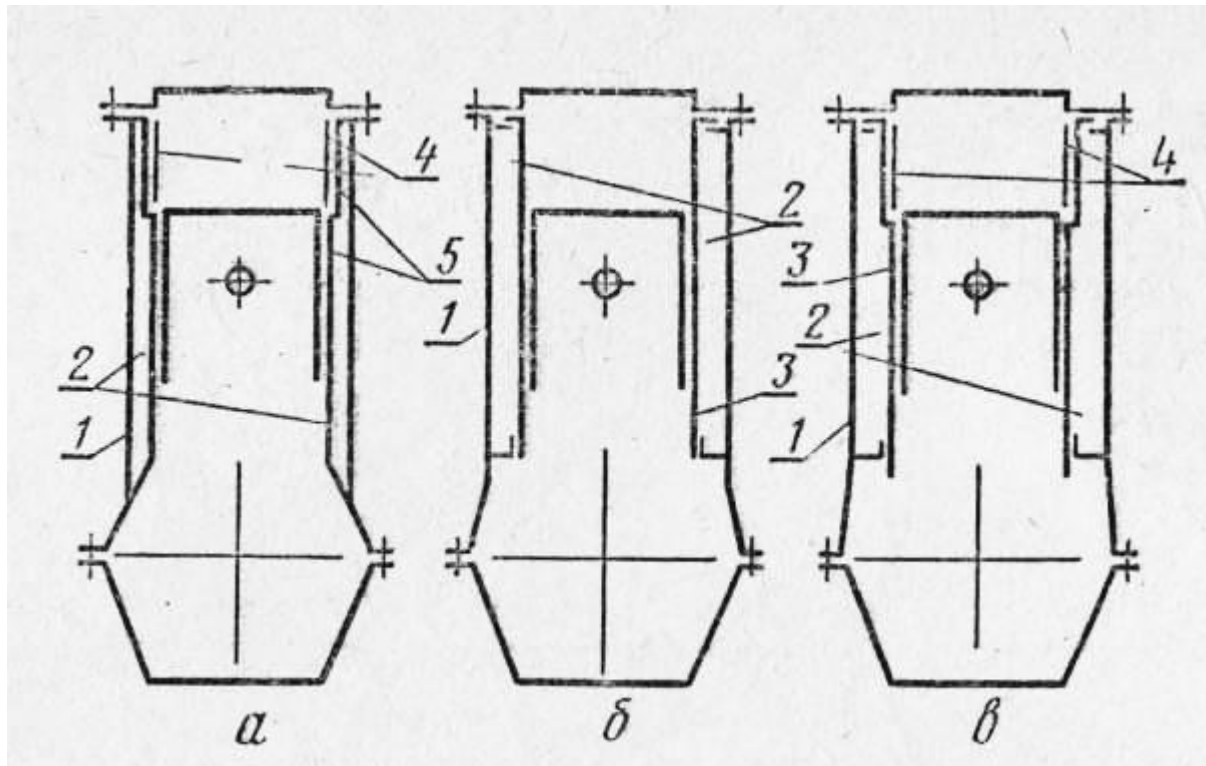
Конструктивные схемы гильз цилиндров: а — цилиндр с короткой сухой гильзой; б — цилиндр с вставной гильзой; в - цилиндр с вставной комбинированной гильзой; 1 — блок-картер; 2 — водяная рубашка; 3 — вставные мокрые гильзы; 4 — сухие гильзы; 5 — цилиндр
